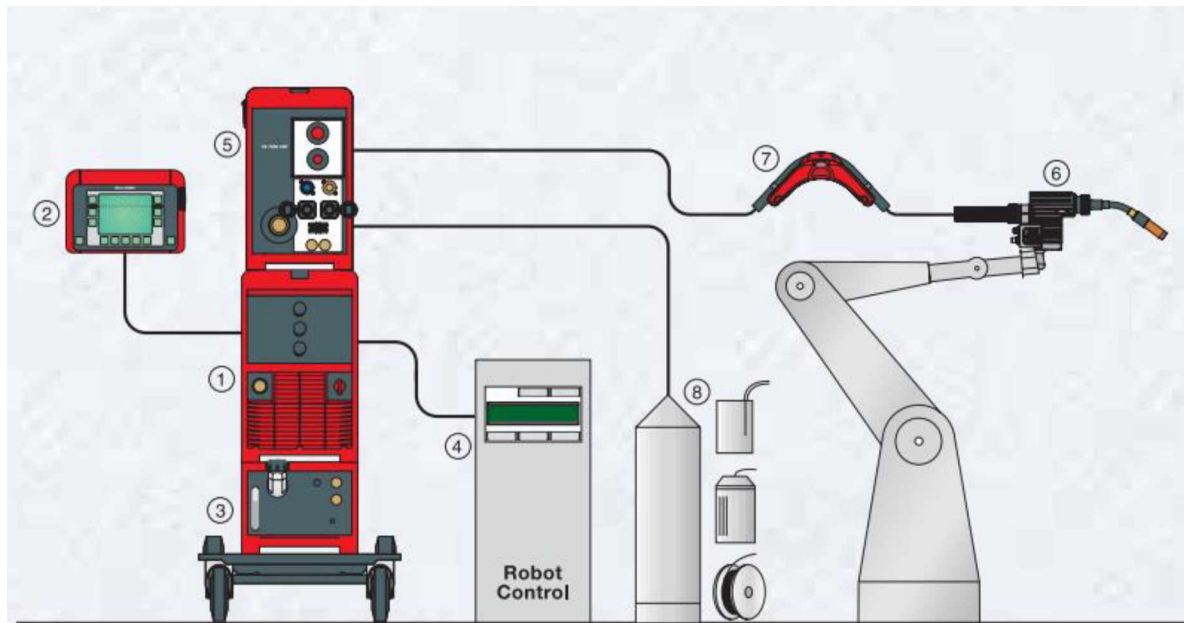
Ilustração do equipamento para soldagem CMT (FRONIUS, 2007)
